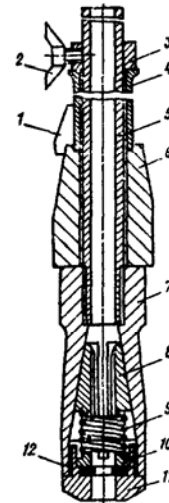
Приспособление для забивки заземлителей вручную:
